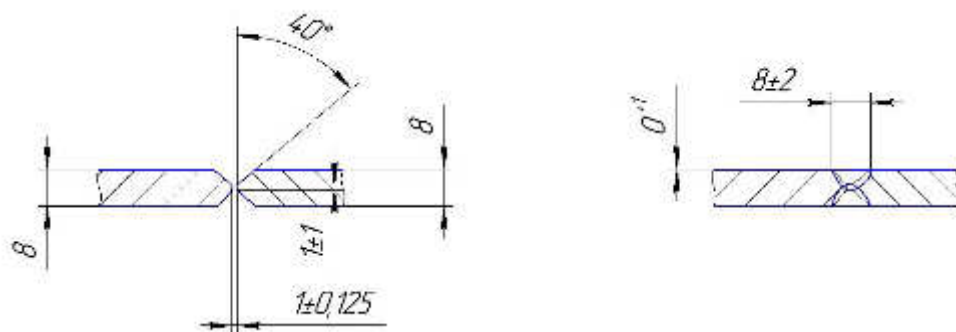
Сварное соединение С25 по ГОСТ 14771-76
